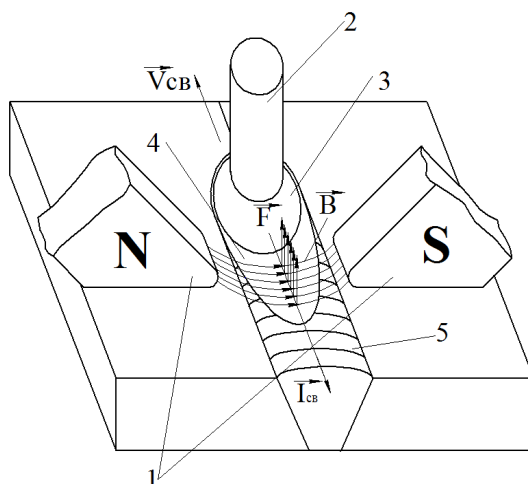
Удержание сварочной ванны поперечным магнитным полем при сварке на обратной полярности. 1 - полюса магнита; 2 - электрод; 3 - дуга; 4 - расплавленный металл; 5 - закристаллизовавшийся металл
